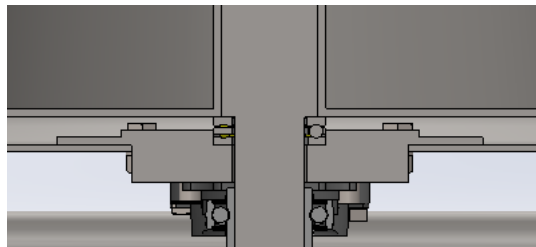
Vista seccionada assemblatge unió rodaments amb l'hèlice
